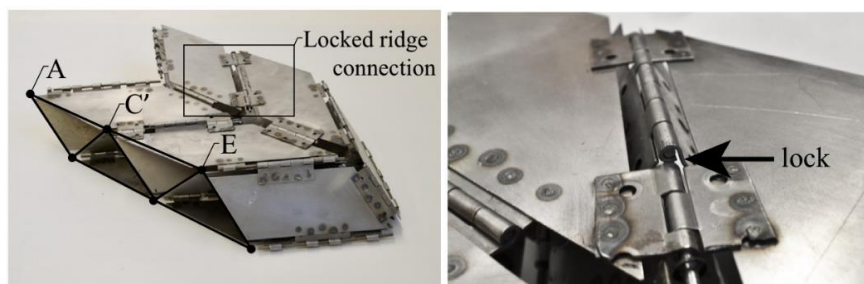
Estrutura Sandwich metálica construída por Gattas and You (2015).
